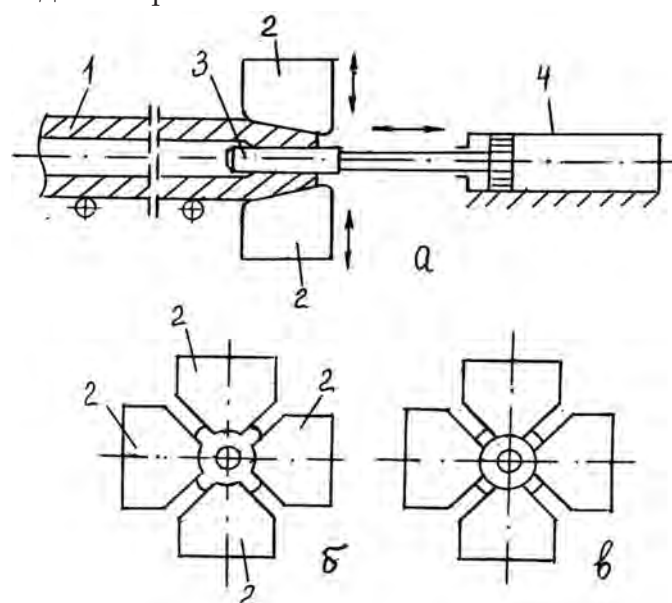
Подготовка переднего конца гильзы на четырехбойковом ковочном прессе:
